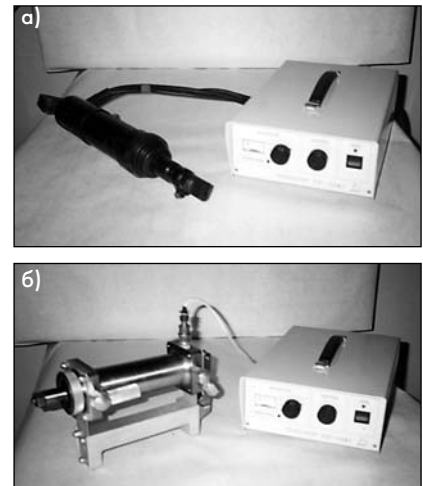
Установка для упрочняющей обработки сварных соединений и тел вращения на ультразвуковой частоте: а — ультразвуковой молоток; б — ударное устройство для суперфинишной обработки тел вращения
